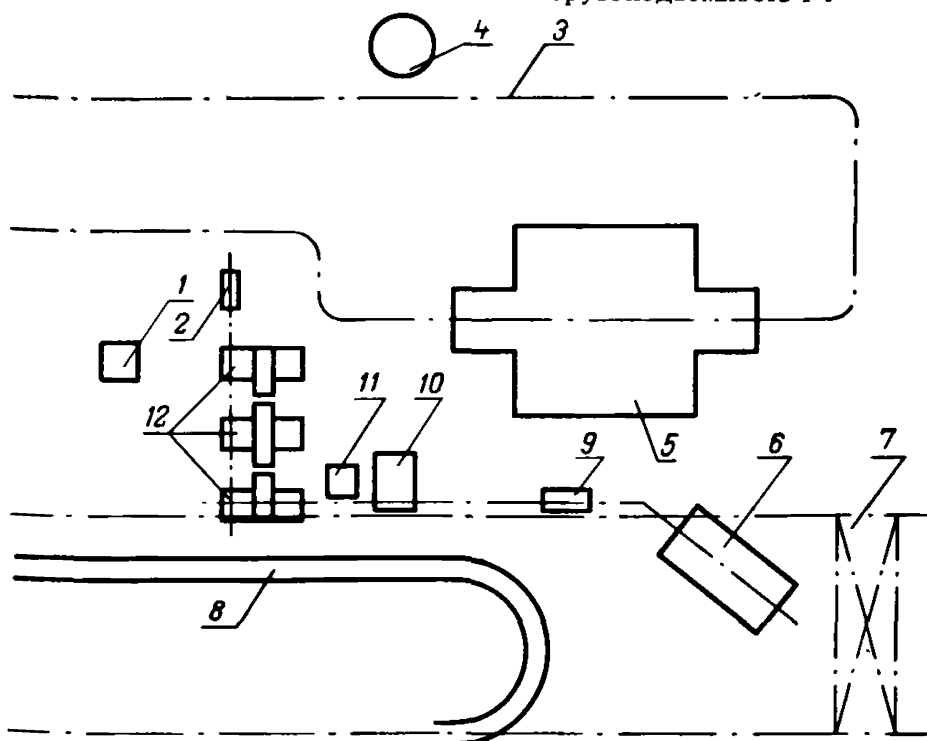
Типовая схема планировки рабочего места разборки двигателя: 1 — тумбочка инструментальная; 2, 9 — электротельфер; 3 — подвесной конвейер; 4 — стенд для разборки двигателя; 5 — моечная машина; 6 — ванна для выварки блока цилиндров; 7 — кран-балка; 8 — конвейер моечной машины; 10 — тара для поршней; 11 — стенд для выпрессовки поршневого пальца; 12 — тележки эстакады
